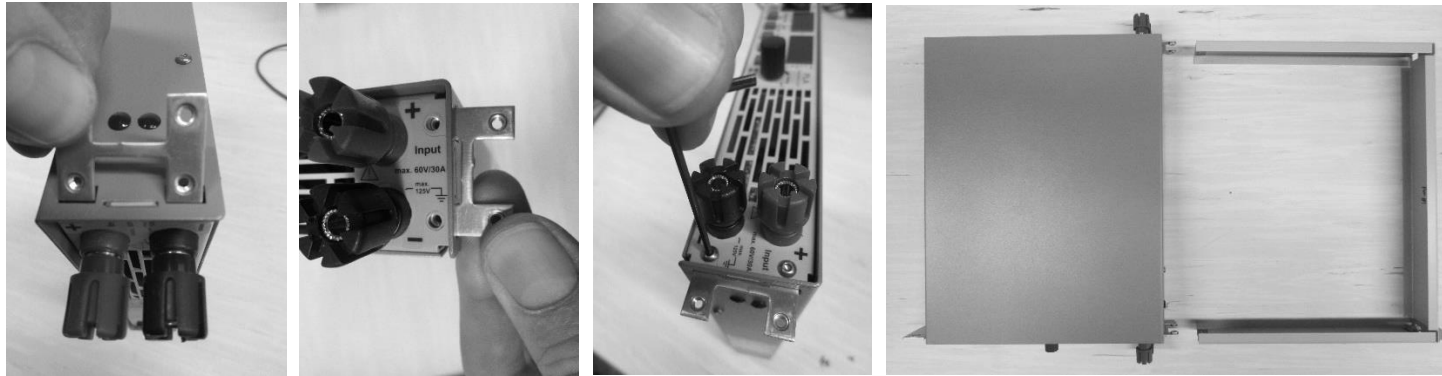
Anschrauben des mittleren Verbindungsteils
